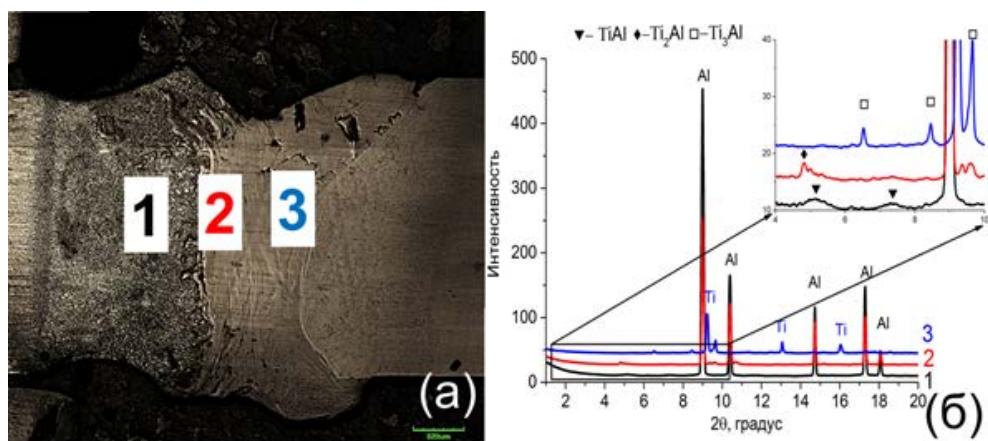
(а) Поперечное сечение разнородного сварного шва (б) дифрактограммы для образца, сваренного без смещения лазерного луча относительно поверхности контакта материалов.
